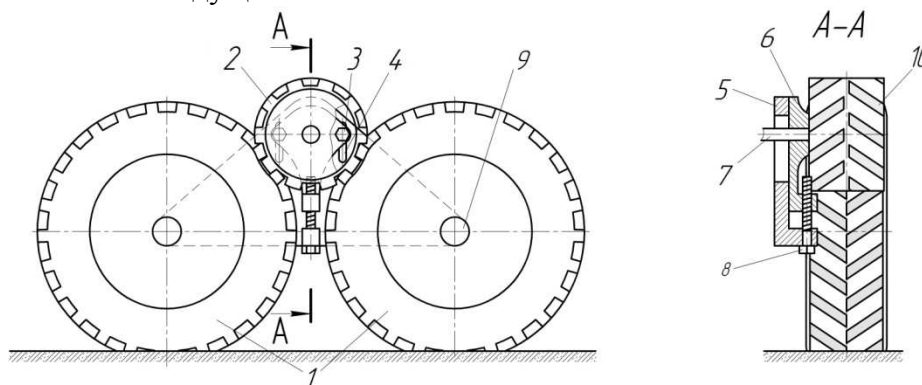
Предлагаемая конструкция роликового привода ведущих колес ТС:
